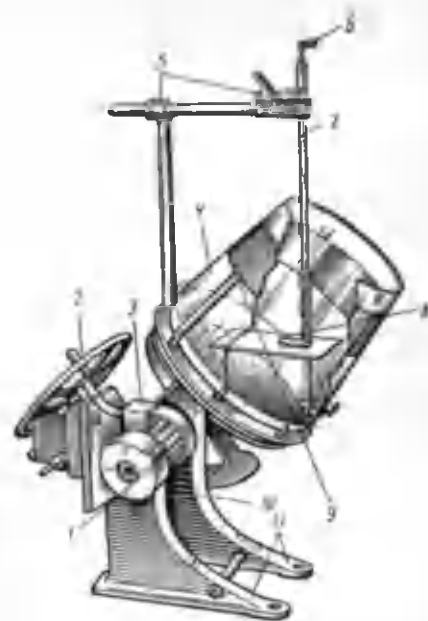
Внешний вид колокола для никелирования корпусов ртутно-цинковых элементов:
